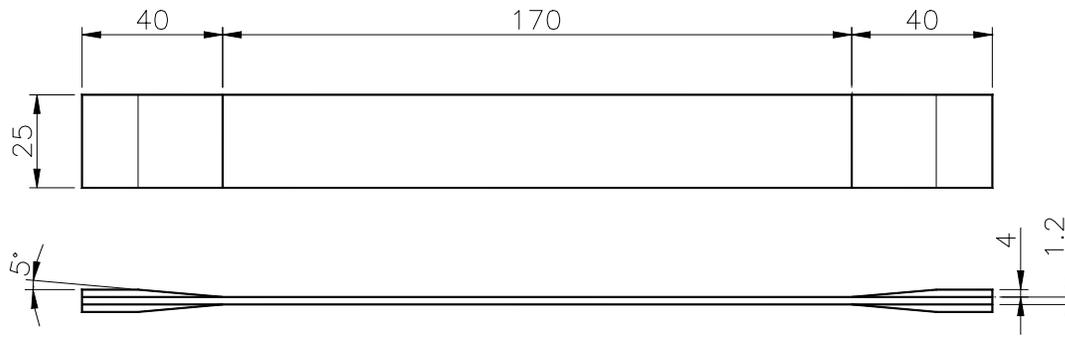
Corpos de prova segundo ASTM 3039/3039 M com as dimensões em mm.
